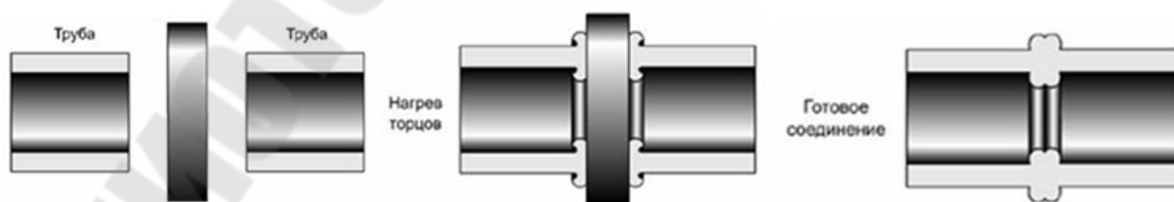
Сварка полимерных трубопроводов контактным нагревом
